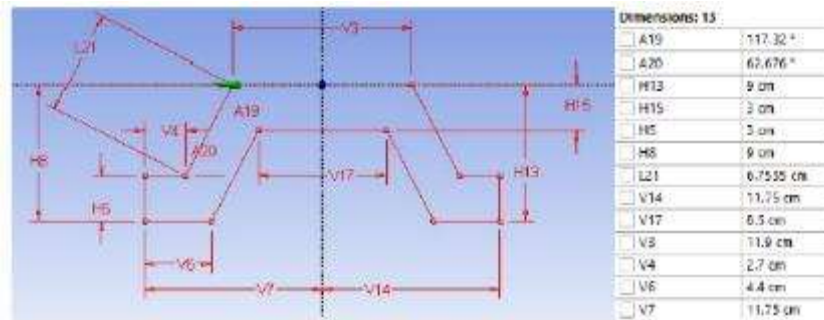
Corte transversal en el plano XZ de la pieza con sus dimensiones [5]
